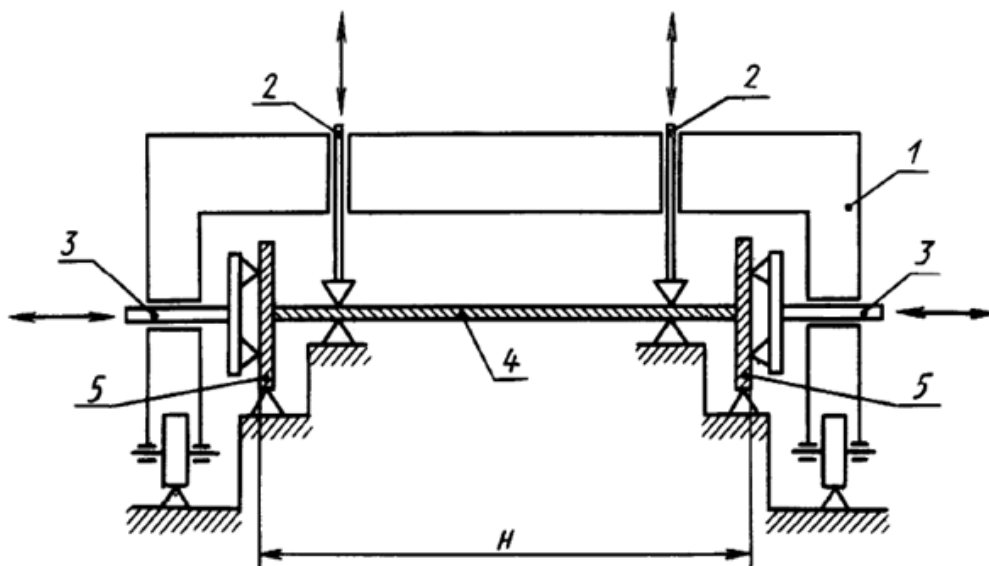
Схема самоходного портала для сборки двутавровой балки:
